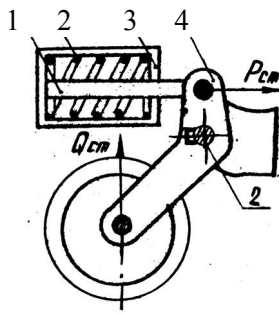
Підресорювання гвинтовою пружиною:
